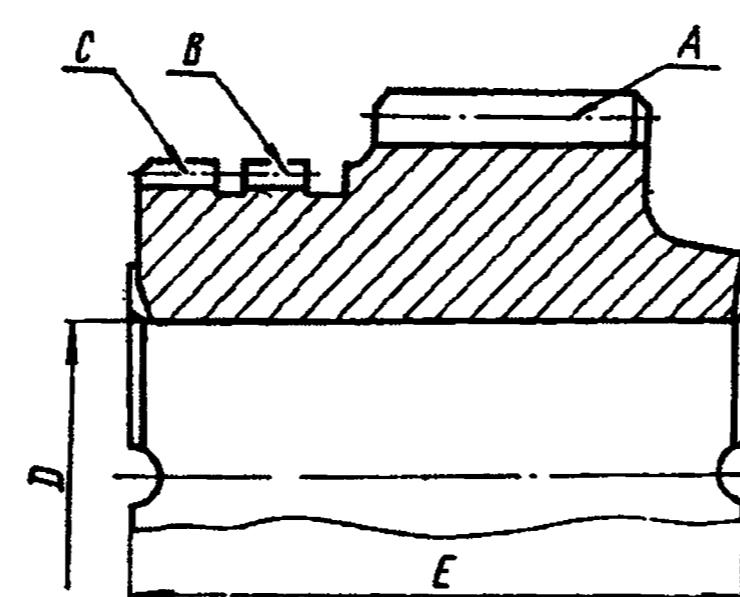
Колесо зубчатое первой передачи промежуточного вала
